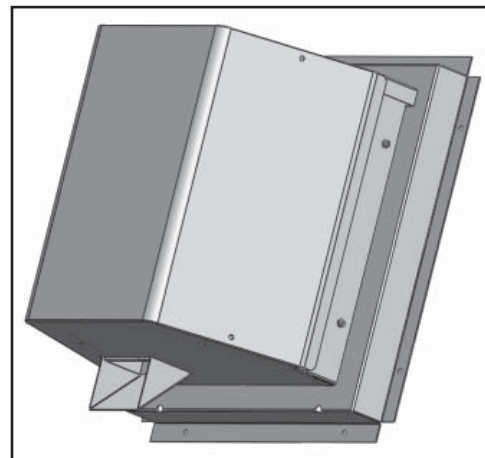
Le couvercle est installé à l'assemblage d'évent forcé.
